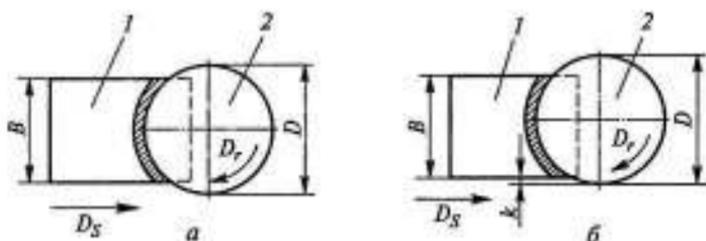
Установка торцевой фрезы относительно заготовки:
